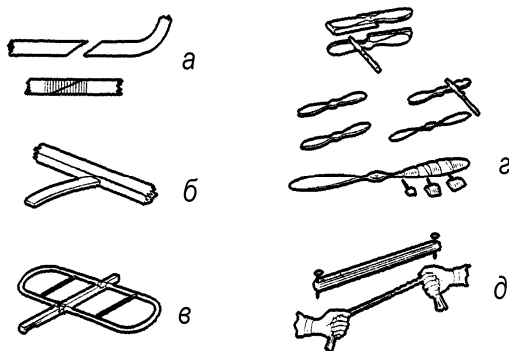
Порядок виготовлення конструктивних елементів схематичної моделі літака: а – з'єднання рейок; б – кріплення нервюр; в – складання стабілізатора; г – виготовлення тягового гвинта; д – виготовлення гумомотора
